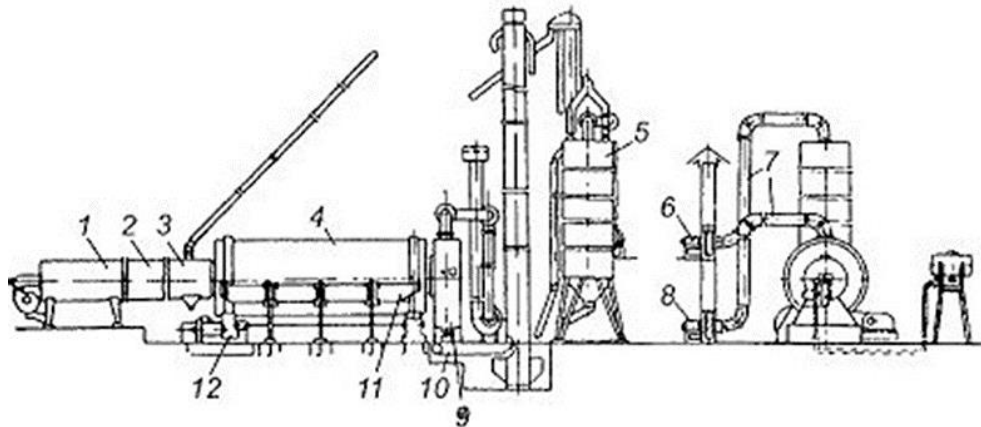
Конструкція зерносушарки барабанної СЗСБ-8А
